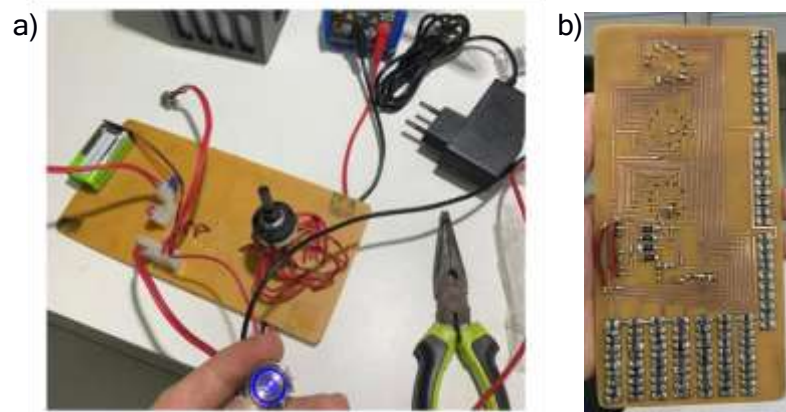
Placa de circuito com as conexões dos fios (a) e a vista frontal com os componentes soldados na placa impressa (b).
